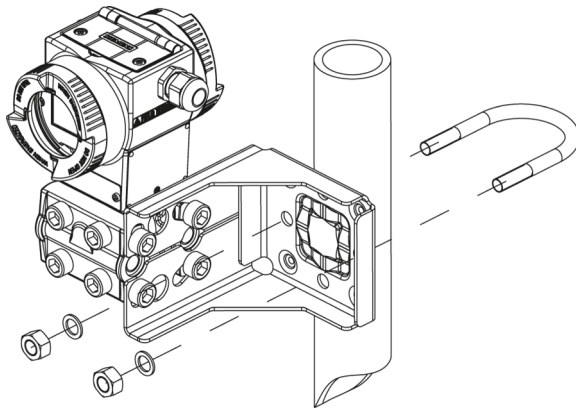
Befestigung des Messumformers mit Montagewinkel für waagrechte Wirkdruckleitungen
